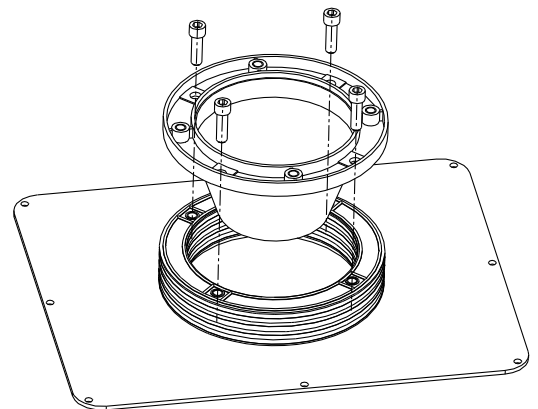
Montage Dämpfungsring DT mit Pumpenträger
